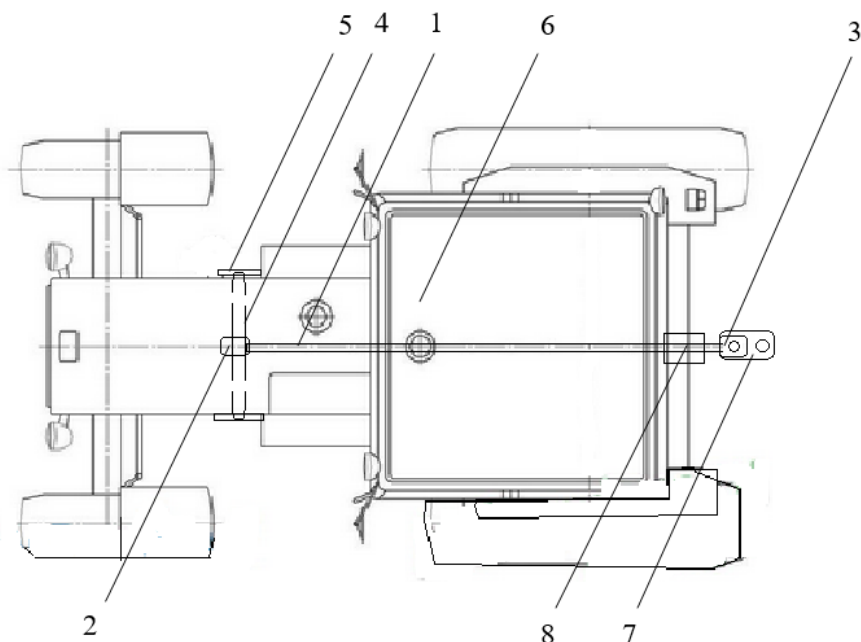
Принципиальная схема буксирно - сцепного устройства с вертикальным регулированием, установленного на колёсный трактор (вид сверху)
